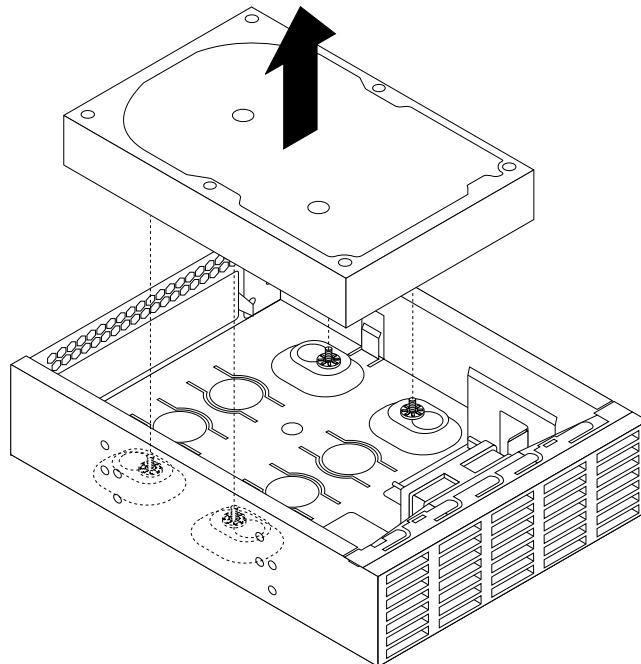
Festplattenlaufwerk aus der Laufwerksadapterhalterung entfernen
